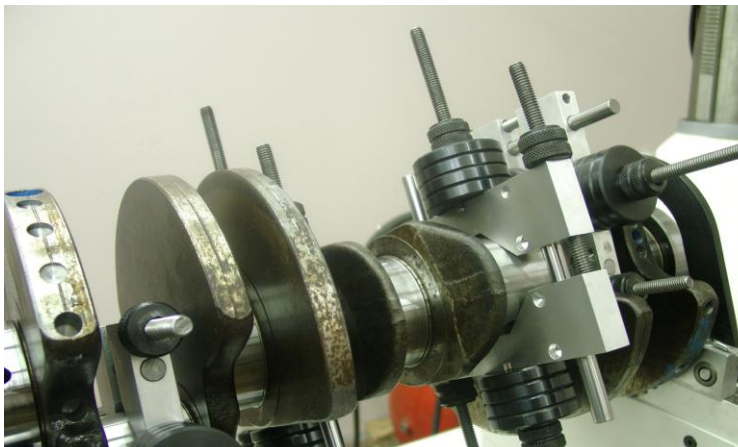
Установка на коленчатый вал грузов, учитывающих различные массы поршней и шатунов
